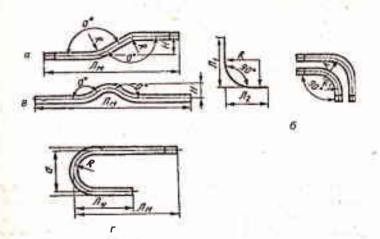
Гнутые детали: a — отступ (утка); б — отводы; в — скоба; г — калач
